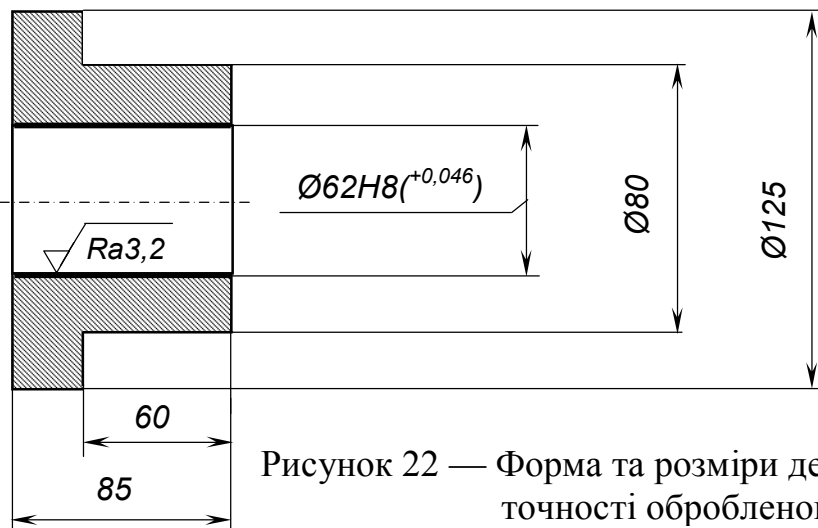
Форма та розміри деталі, показники точності обробленого отвору
